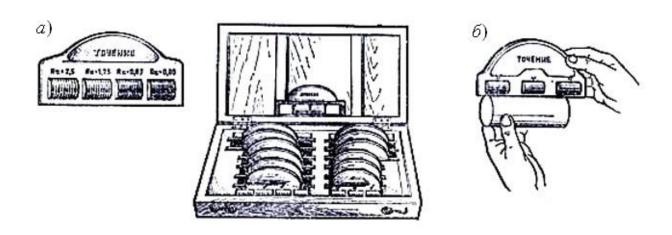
Общий вид образцов шероховатости поверхности (a) и пример сравнения (δ)
